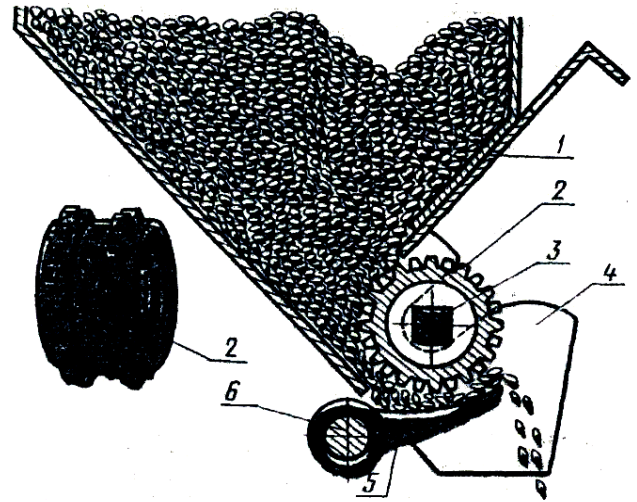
Катушечно-штифтовой труковысевающий аппарат: 1 – задвижка; 2 – катушка; 3 – вал труковысеющих аппаратов; 4 – корпус; 5 – доннышко; 6 – вал доннышек
